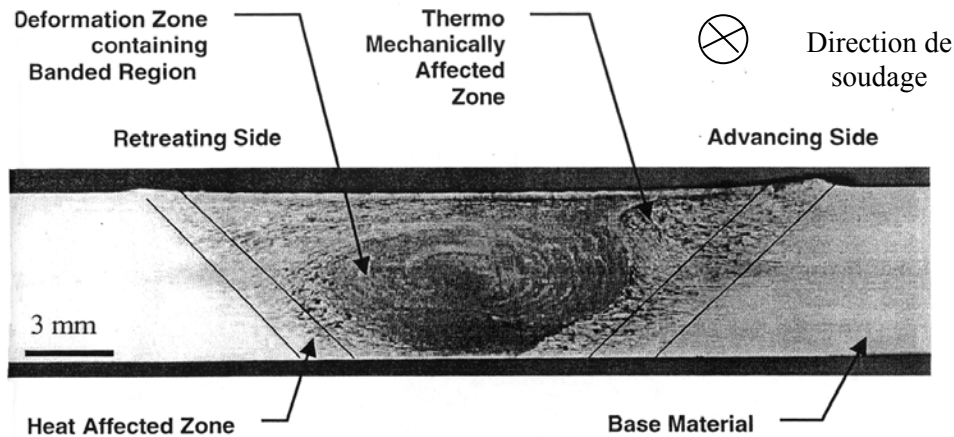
Profil d'un joint soudé selon une coupe perpendiculaire à la direction de soudage [TWI]
